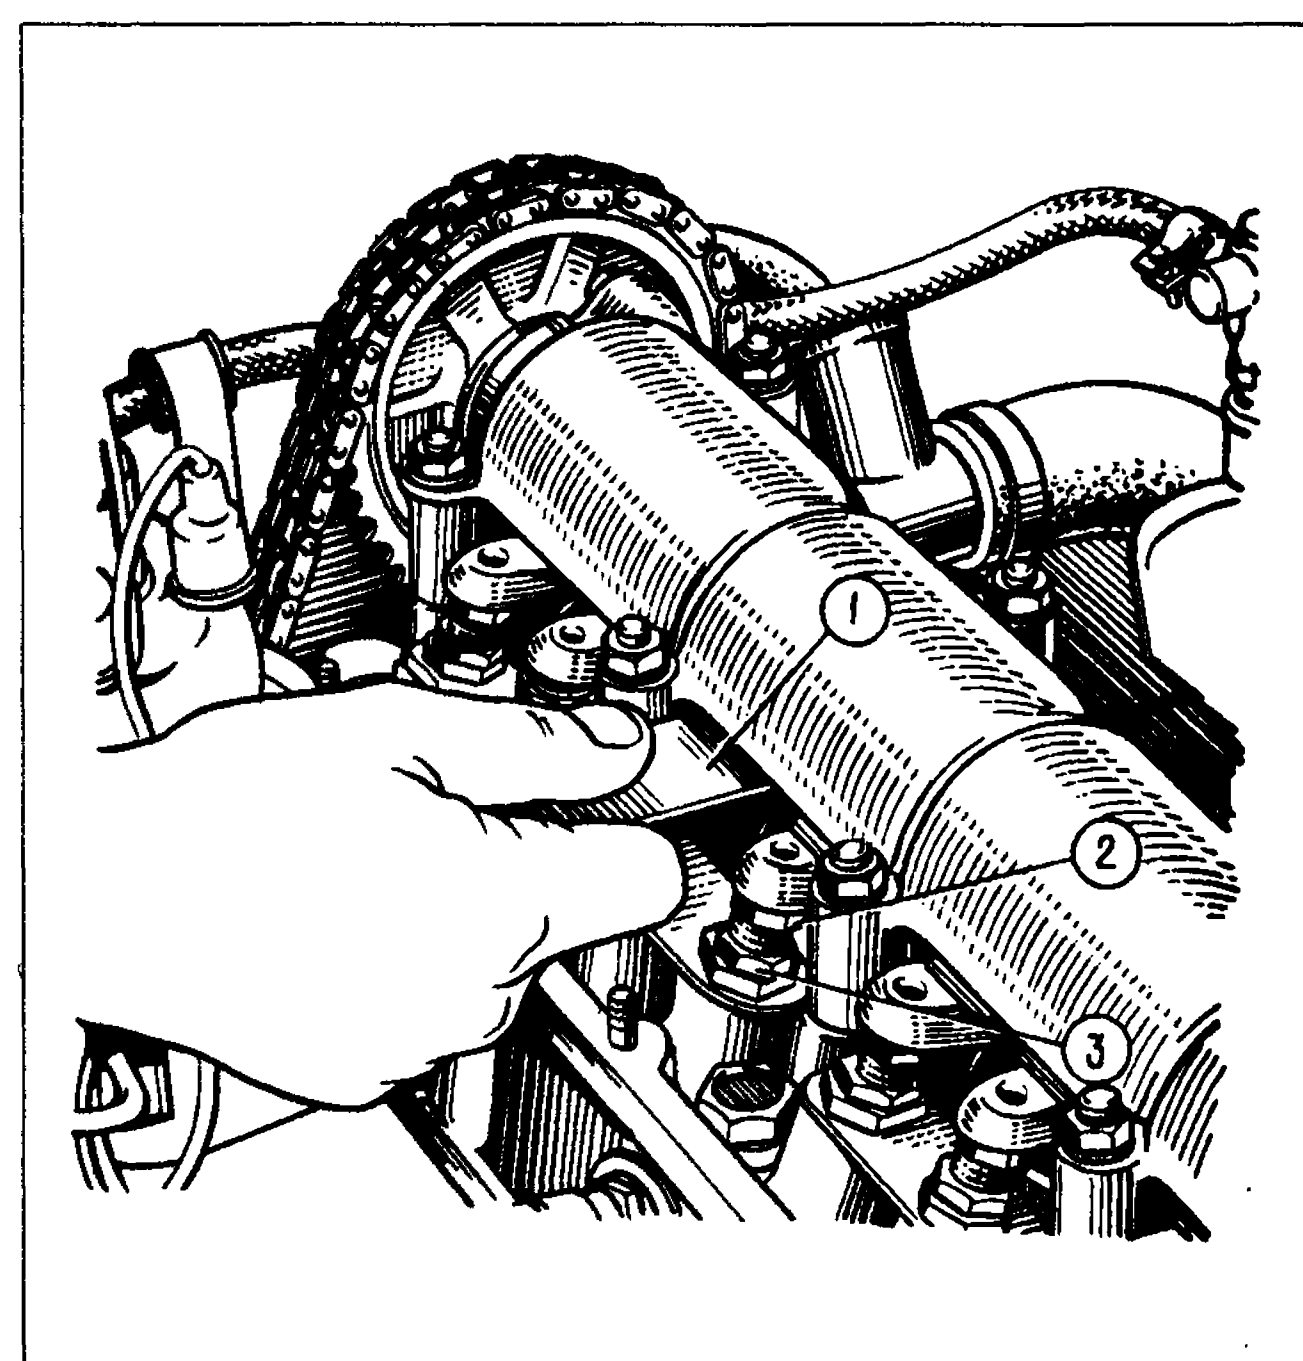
Проверка зазора между рычагами и кулачками распределительного вала: 1 - шуп А.95111; 2 - регулировочный болт; 3 - контргайка регулировочного болта
